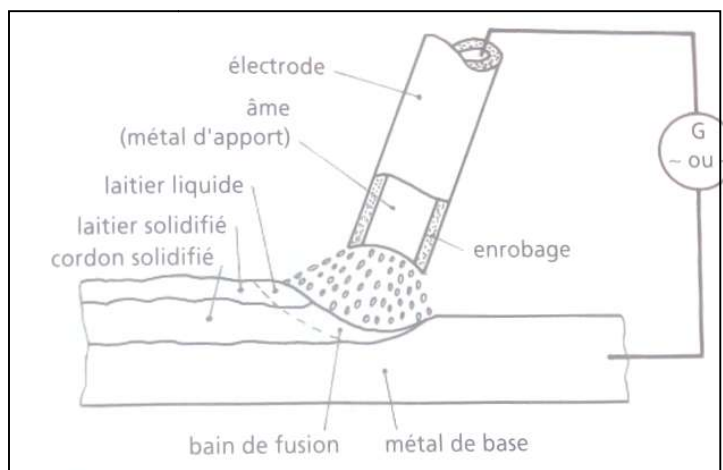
Soudage à électrode enrobée [6]
